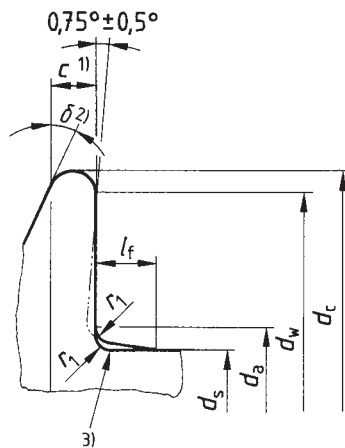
Sechskantschraube mit Flansch — Vollschaft (Regelausführung)
